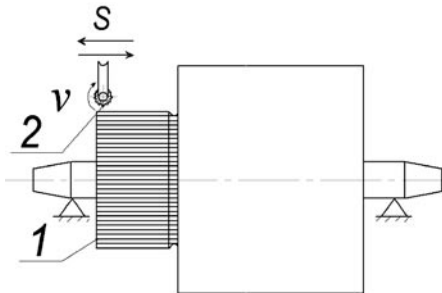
Схемы установки якоря при обработке коллектора дисковой фрезой:
